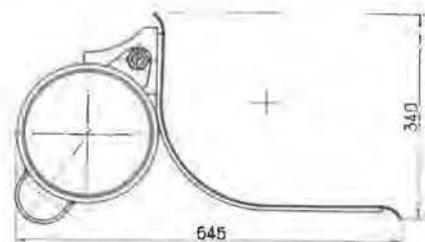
Coupe montrant l'assemblage des couloirs de glissement au tube de retour de la chaîne à disques. Assemblage dit « couloirs équerres ».
